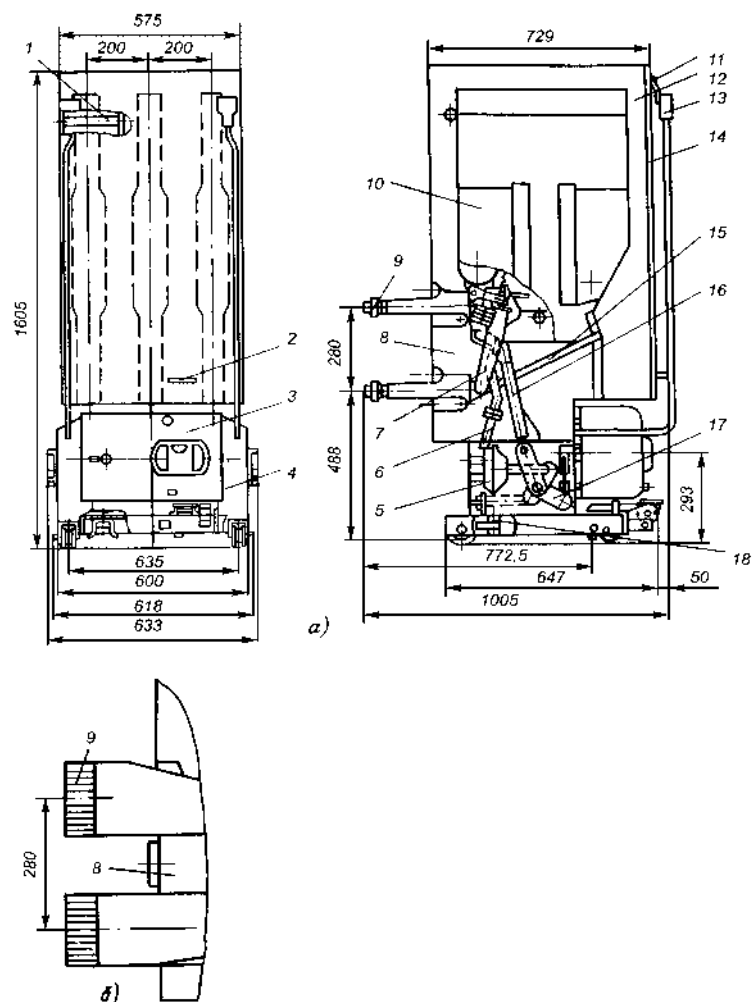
Выключатель электромагнитный ВЭ-10: а) – на номинальный ток дотя 2500 А; б) – контакт выключателя на номинальный ток 3600 А: 1 – распорка; 2 – ручка; 3 – привод; 4 – основание; 5 – устройство дутьевое; 6 – трубка; 7 – контакт подвижный; 8 – полюс; 9 – контакт подвижный выдвигного элемента КРУ; 10 – камера; 11 – скоба; 12 – кожух; 13 – разъём штепсельный; 14 – лист; 15 – шина; 16 – тяга; 17 – вал выключателя
